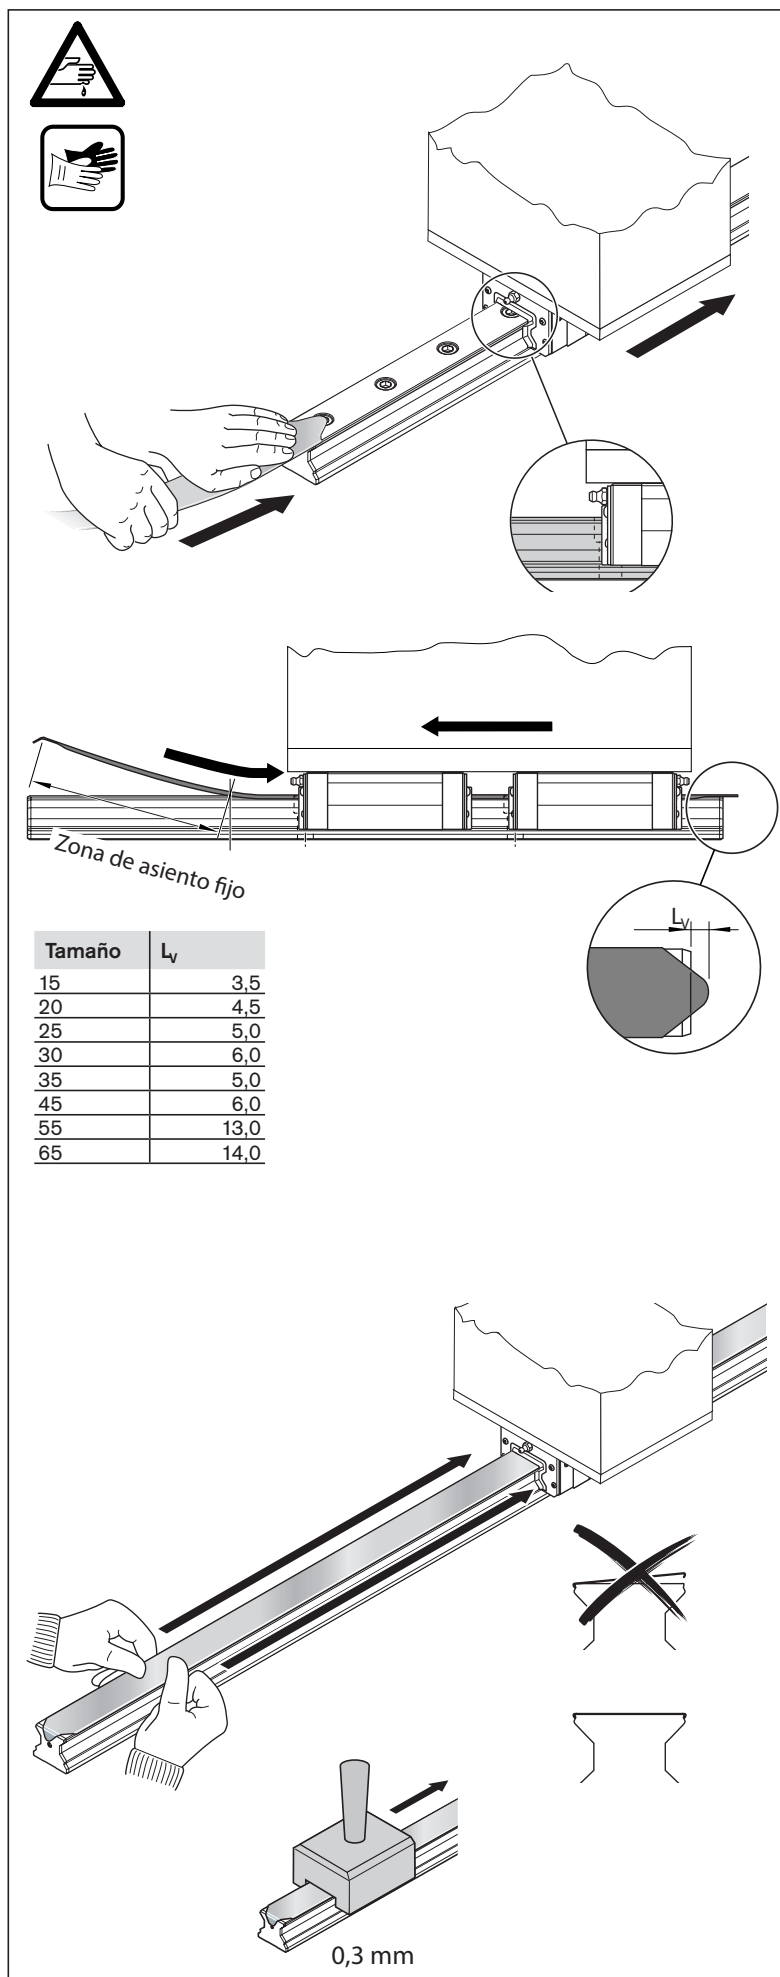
Montaje de bandas de protección con zona de deslizamiento
